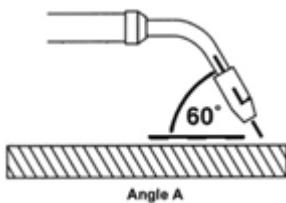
Положение сопла горелки при сварке, угол А
